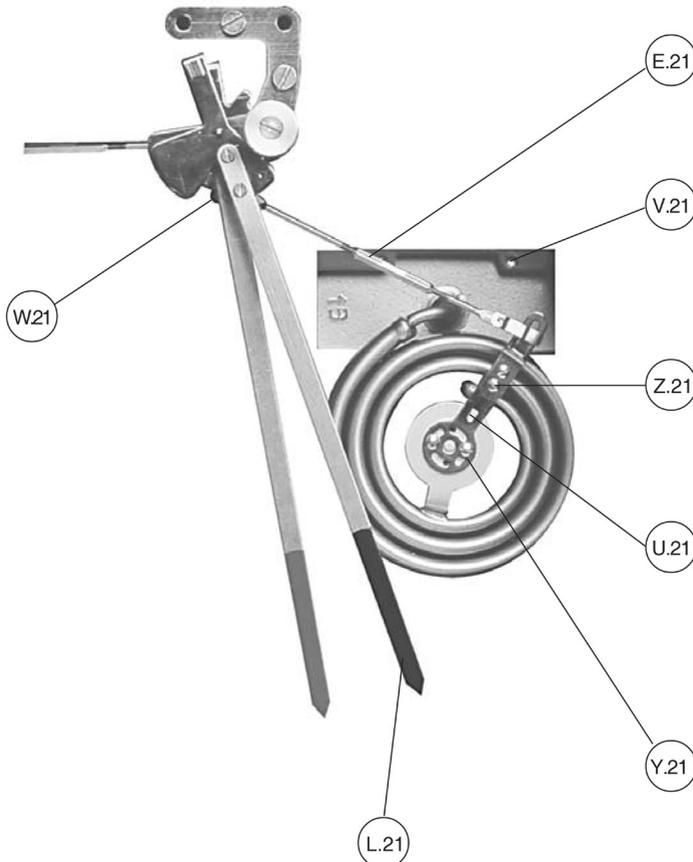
Elemento di misura con molla spirale (manometrica o termometrica)
